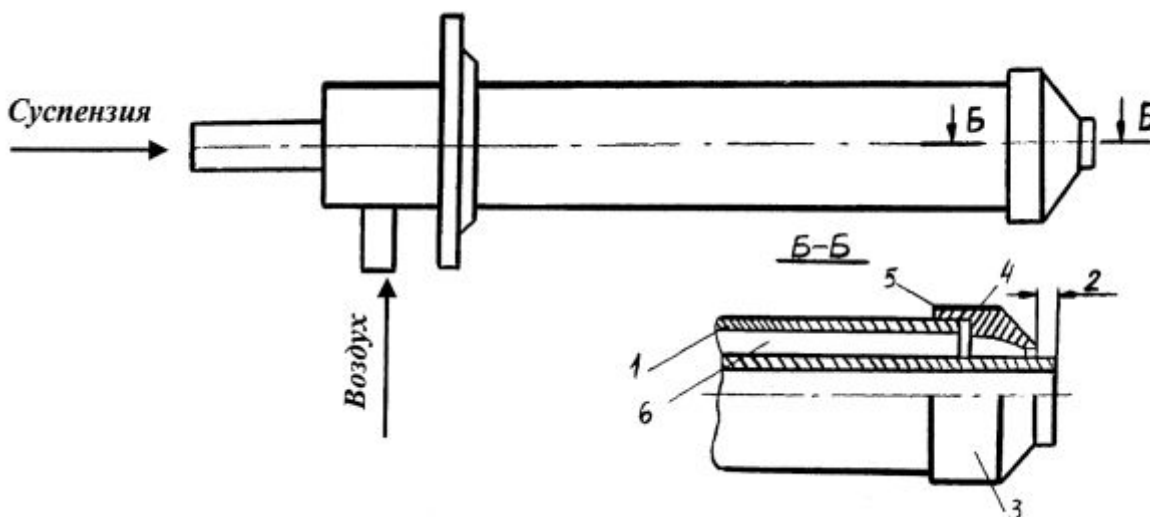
Конструкция пневматической форсунки: 1 – корпус; 2 – патрубок; 3 – втулка; 4 – шайба центровочная; 5 – сопло; 6 – трубка подачи суспензии.
